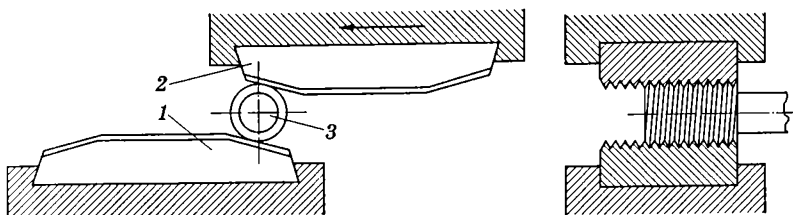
Схема накатывания резьбы на накатном станке:
